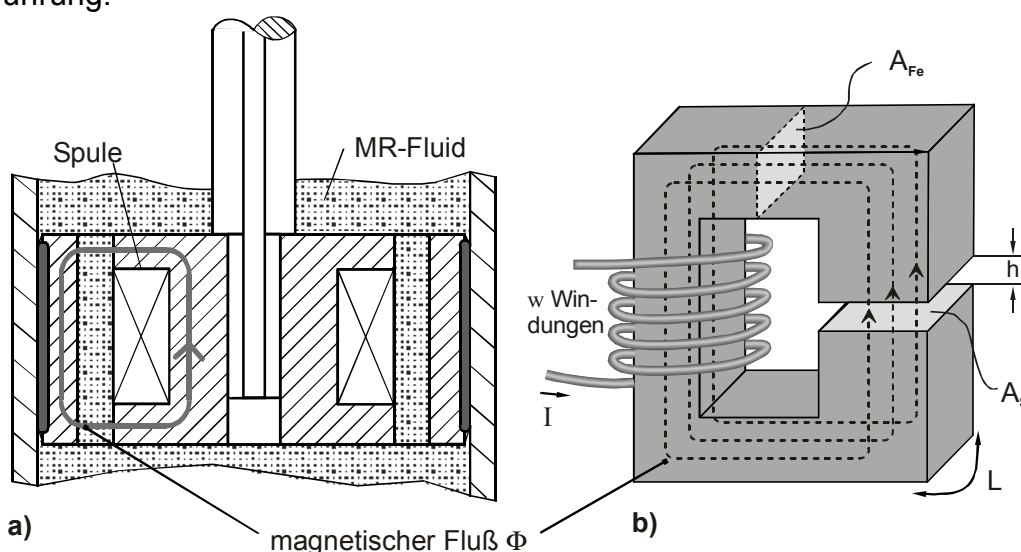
a) Schnitt durch einen Dämpferkolben
